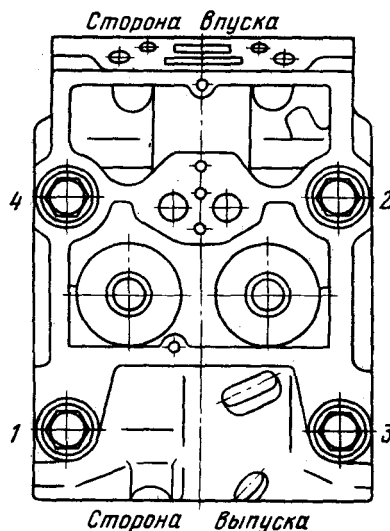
Порядок затяжки и отвинчивания болтов крепления головки цилиндров
